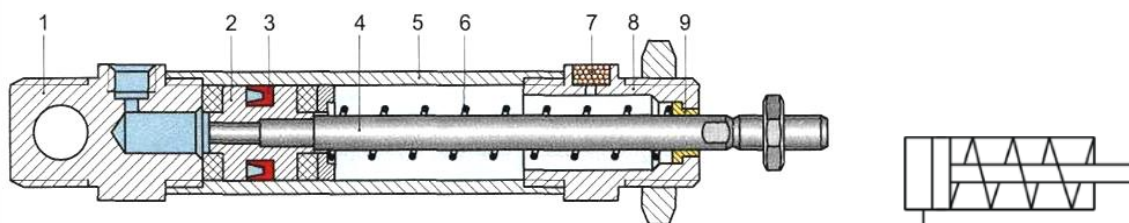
Пневмоцилиндр одностороннего действия: 1 – задняя крышка; 2 – поршень; 3 – уплотнение; 4 – шток; 5 – корпус; 6 – пружина; 7 – отверстие с фильтром; 8 – передняя крышка; 9 – направляющая втулка
